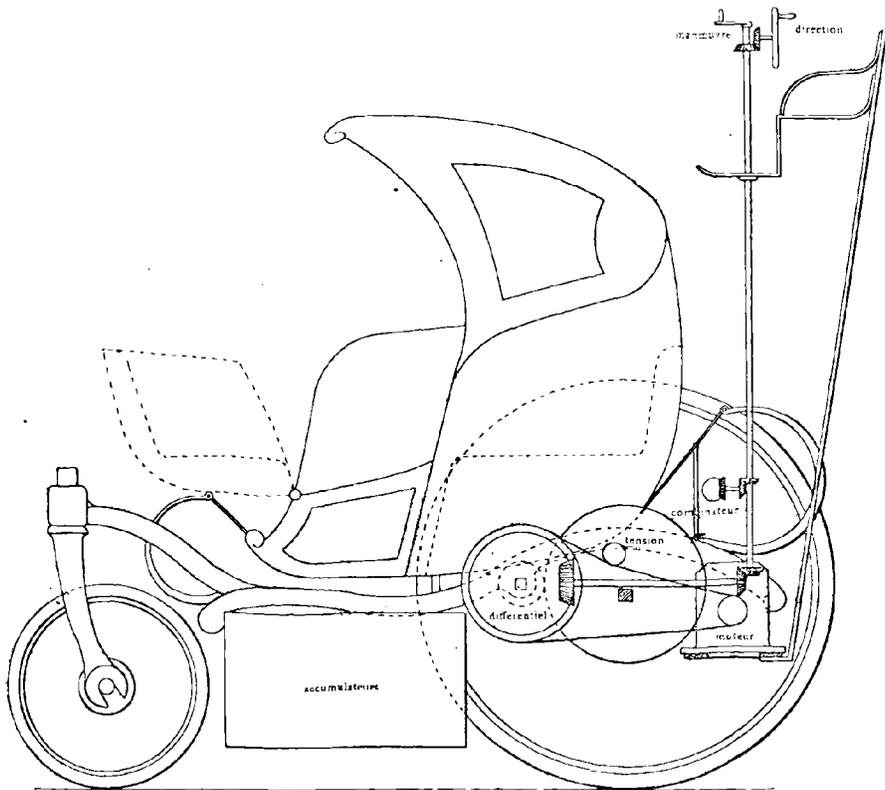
Voiture Vedovelli et Priestley (Élévation).
